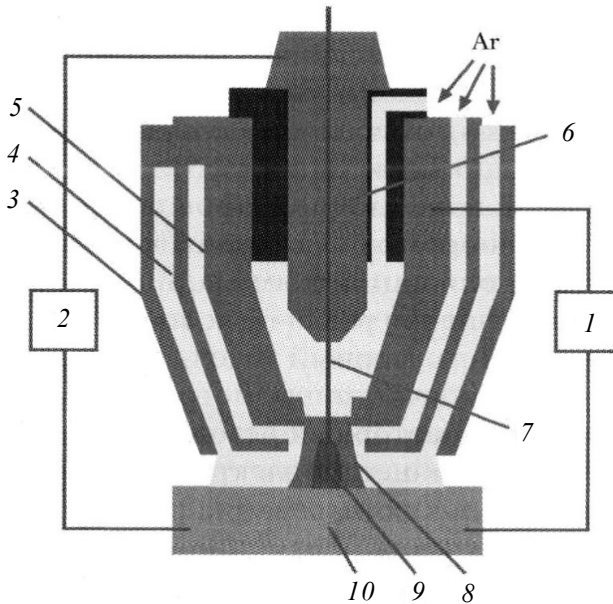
Схема процесу гібридного плазмодугового зварювання плавким електродом:
